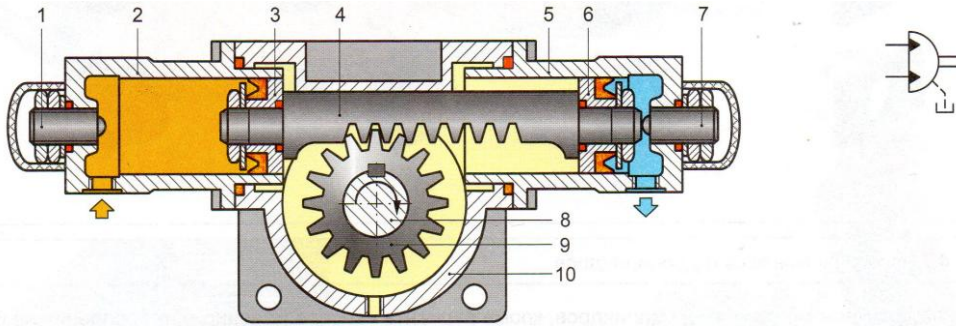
, б. Поршневой ПГД с реечной передачей: 1, 7 – регулировочные винты; 2, 5 – гильзы; 3, 6 – поршни; 4 – рейка; 8 – выходной вал; 9 – шестерня; 10 – корпус гидродвигателя.
